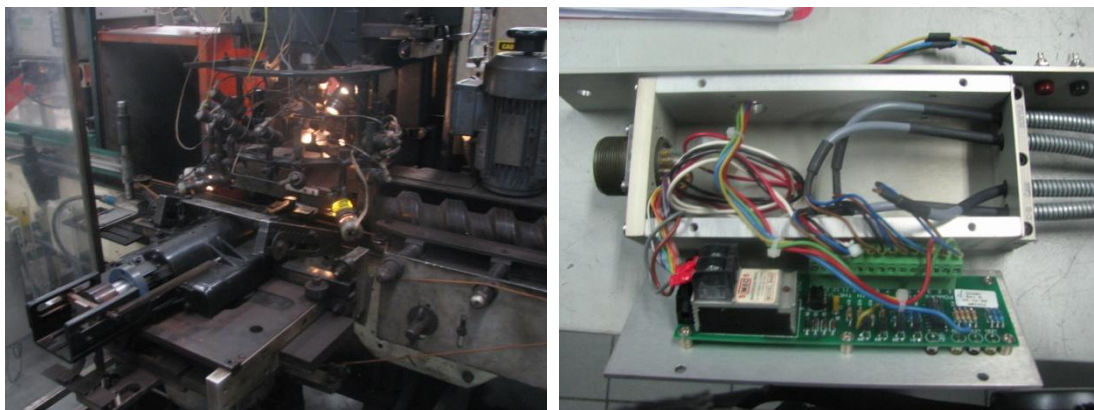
Máquina de inspecção Combi Esquerda da linha 11 com detector de garrafa em destaque
